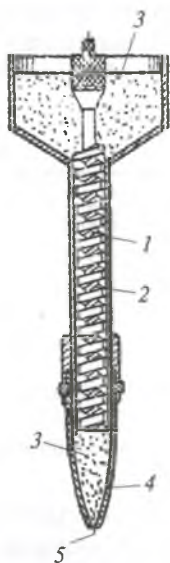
Схема устройства для подачи присадочного армирующего материала в сварочную ванну
